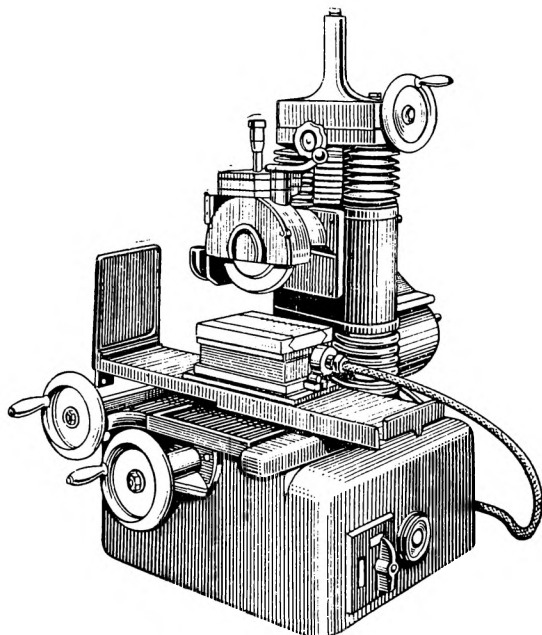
Настольный плоскошлифовальный станок высокой точности с магнитным столом
